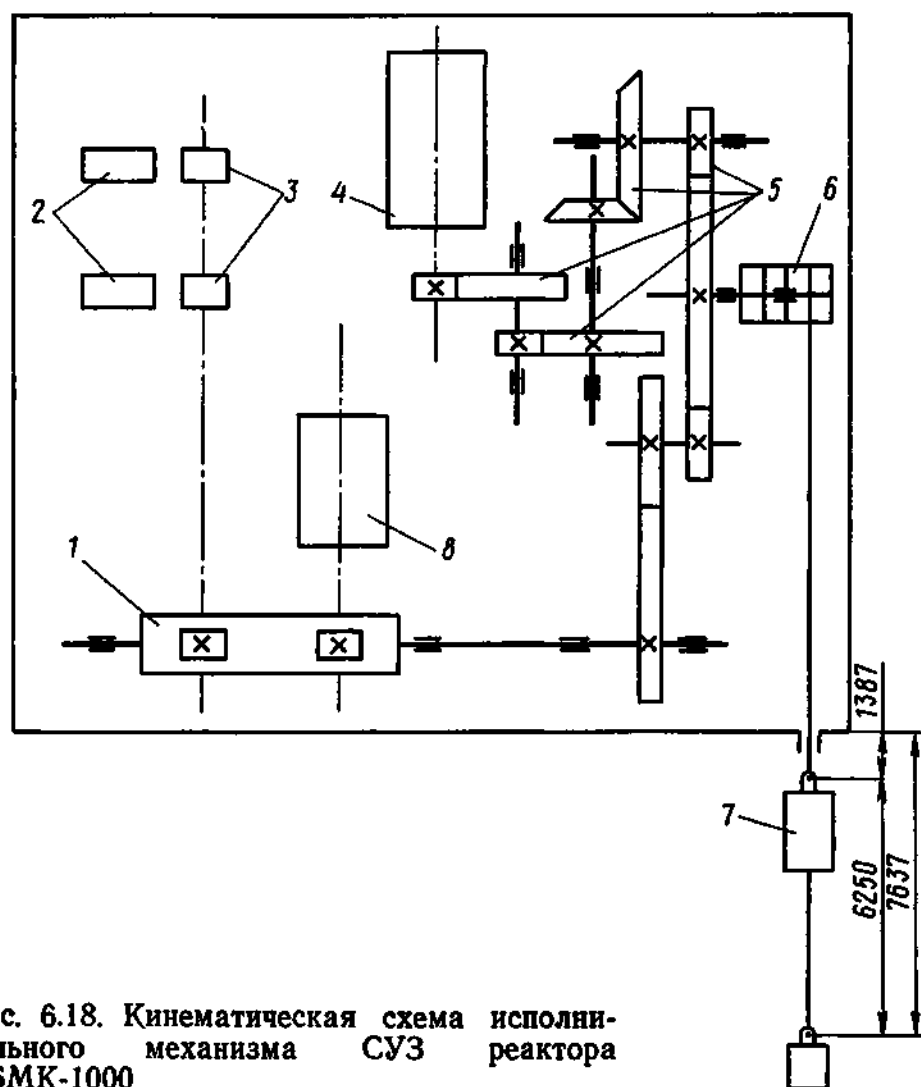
Кинематическая схема исполнительного механизма СУЗ реактора РБМК-1000
